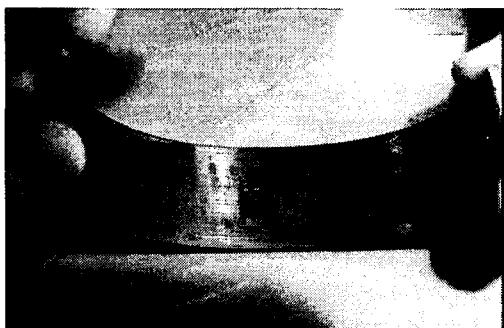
성능시험을 마친 후의 Radial gas bearing의 top foil 상태
